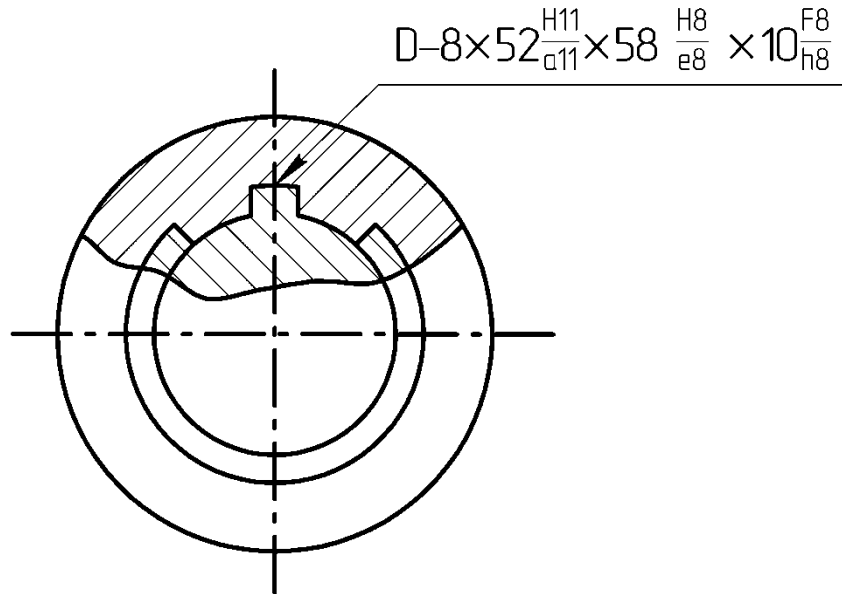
Обозначение посадок на сборочном чертеже шлицевого соединения
